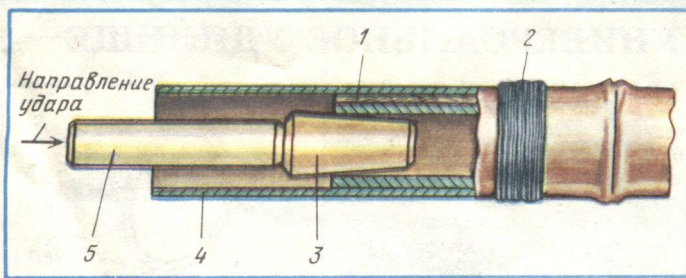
Крепление соединительной втулки: 1 — накладка; 2 — намотка из стеклянной нити; 3 — конусная пробка; 4 — втулка; 5 — бойк.
